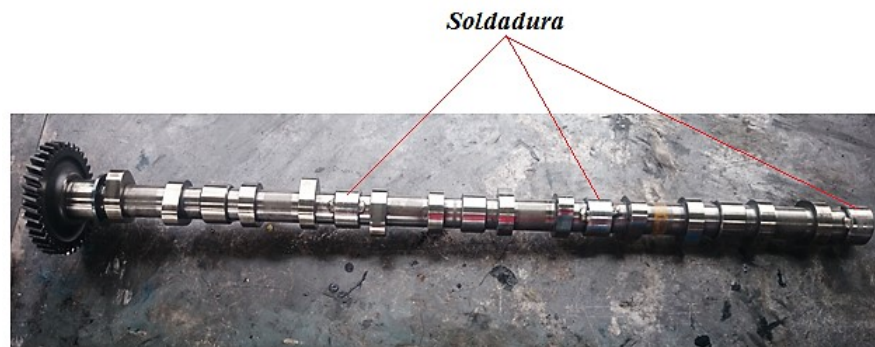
Soldadura en el árbol de levas de un motor diésel de 6 cilindros.
